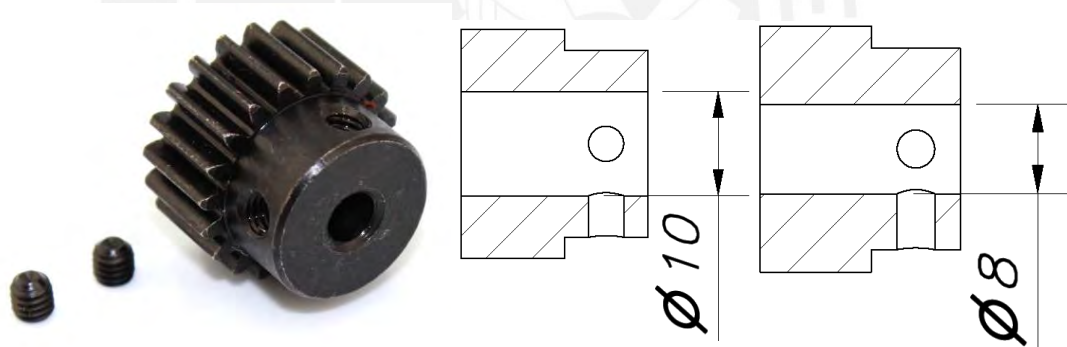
Engranaje F17650 JMT<sup>11</sup>, planos del engranaje de 10 mm y 8 mm de diámetro interno
